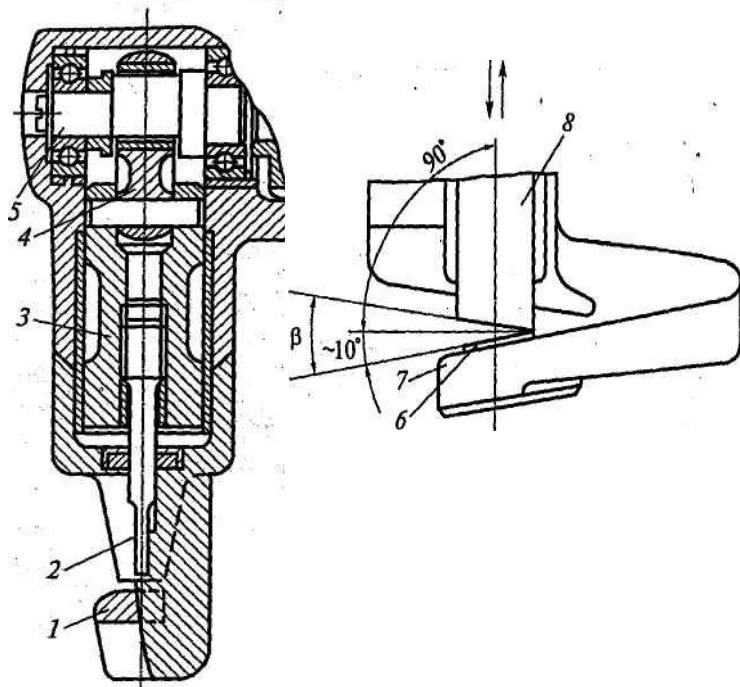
Вырубные ножницы (а) и режущая головка ножевых ножниц (б)
